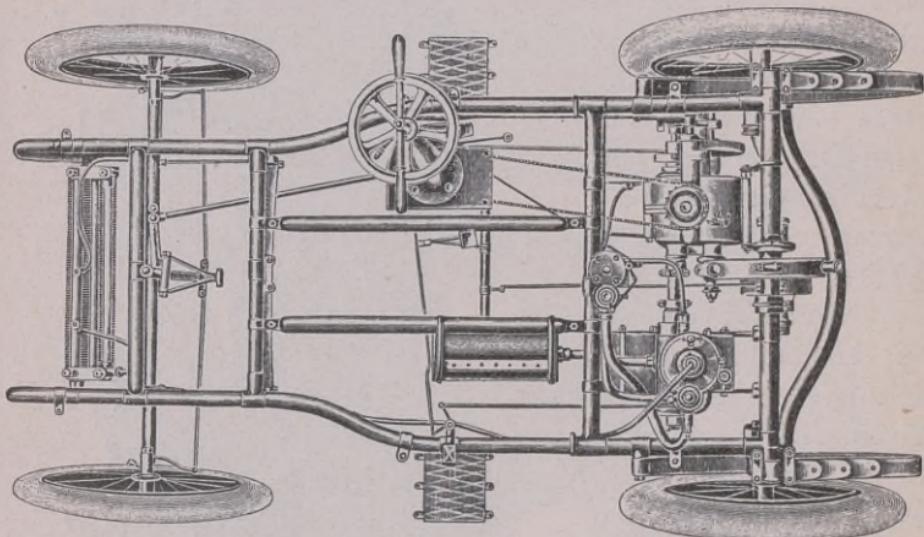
Voiturette ($4\frac{1}{2}$ HP) im Grundriss.
